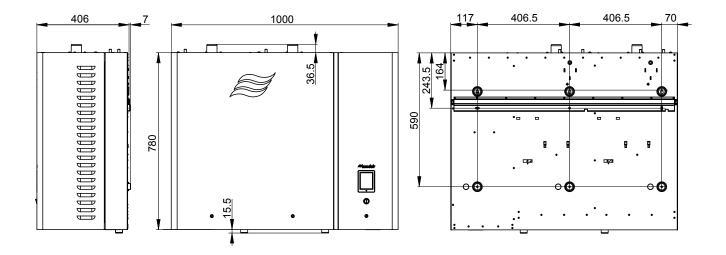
Dimensions Condair EL 20 - 45 et EL 35 - 180, taille de boîtier "M" (mesures en mm)
